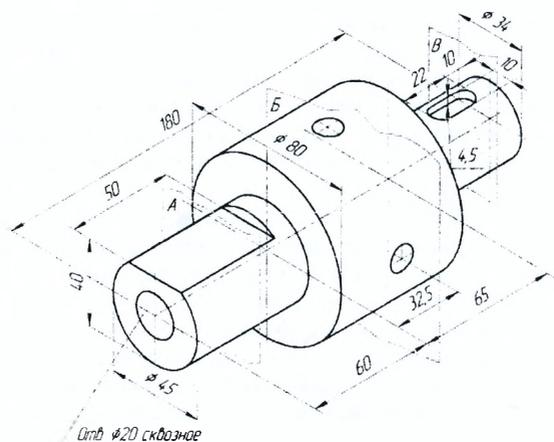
Построение чертежа детали по аксонометрическому изображению
